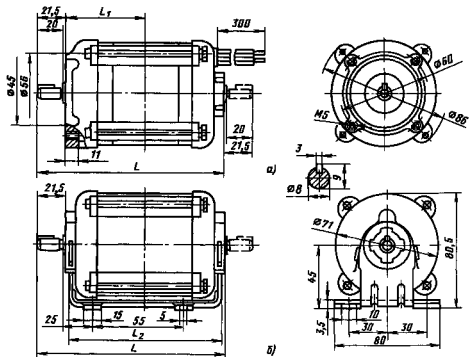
Габаритные и установочные размеры двигателей АВЕ 04-го габарита
